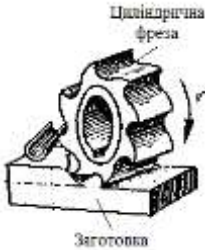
Схема фрезерування циліндричною фрезою
